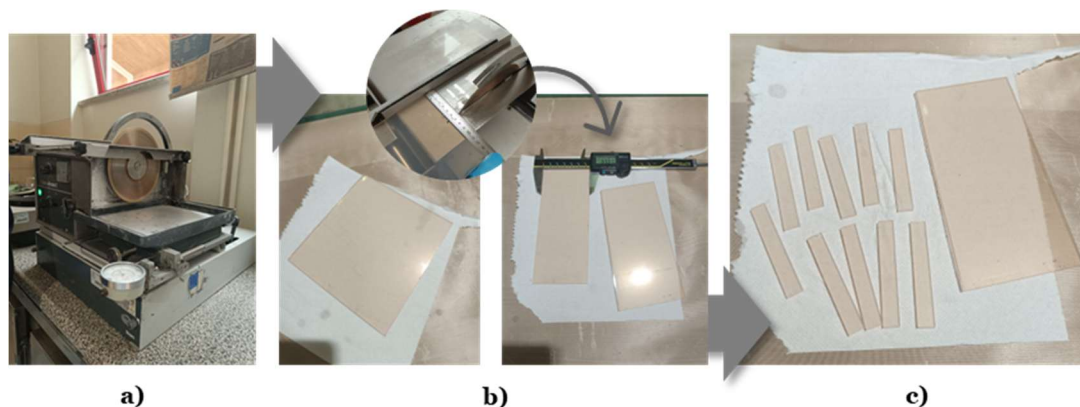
Processo de Corte dos Provetes: a) Equipamento *Struers Accutom 2*; b) Corte da matriz; c) Corte dos Provetes
